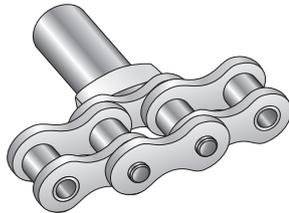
Anbauteil Typ D5 (langer Bolzen)
